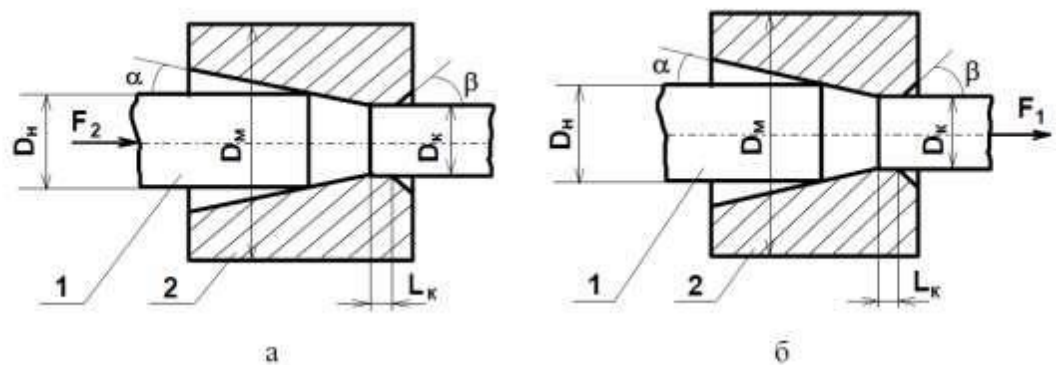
Технологічні схеми включають деформування за схемою стиску (а) і напруження (б) заготовки (1 – заготовка; 2 – матриця).
